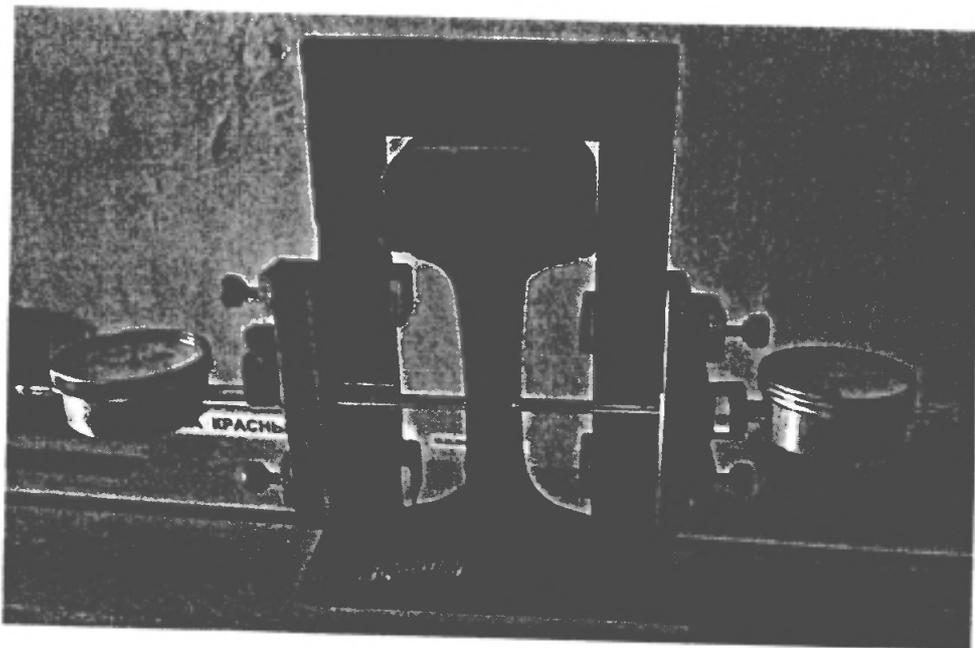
Приспособление РБ 61.61.П.6 для определения толщины шейки рельса
